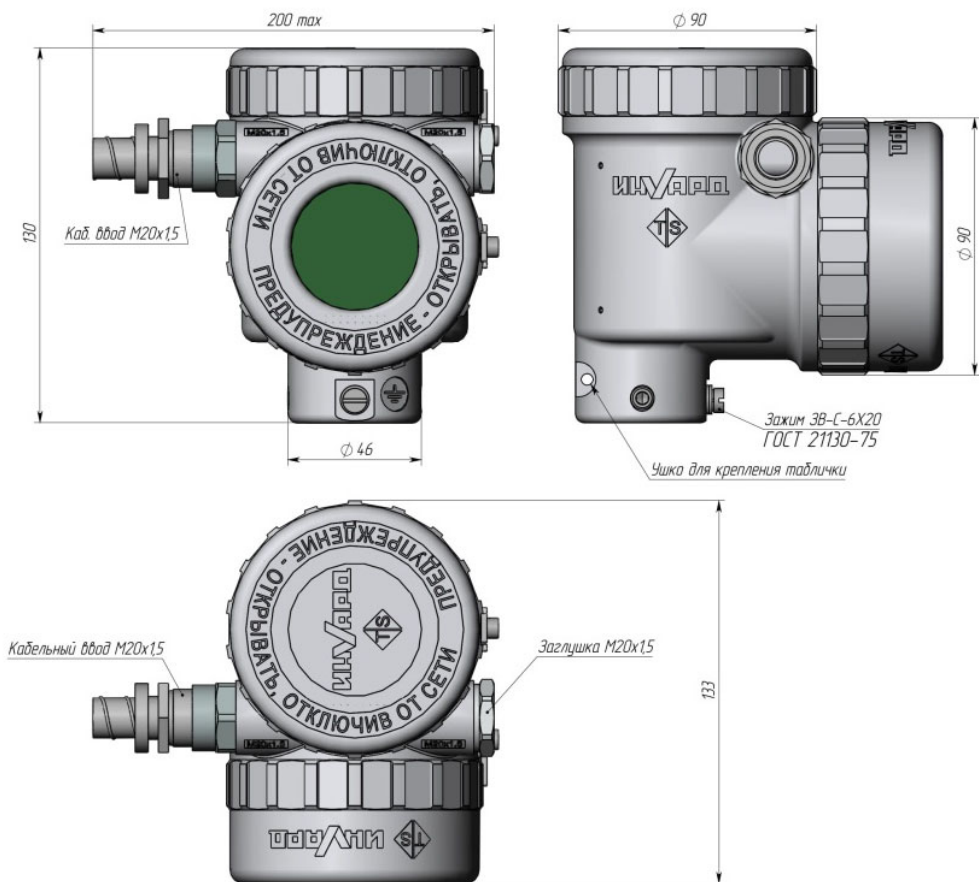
Габаритные и установочные размеры алюминиевого мини корпуса блока электронного преобразователя. IP67. Дисплей сверху
